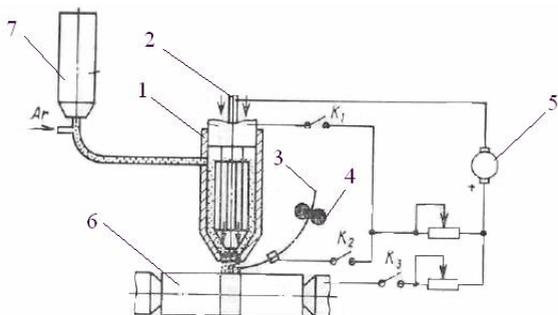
Схема установки плазменной наплавки комбинированным способом: 1 – корпус плазмотрона (анод); 2 – вольфрамовый электрод; 3 – электродная проволока; 4 – механизм подачи проволоки; 5 – источник питания; 6 – наплавляемая деталь; 7 – порошковый питатель
